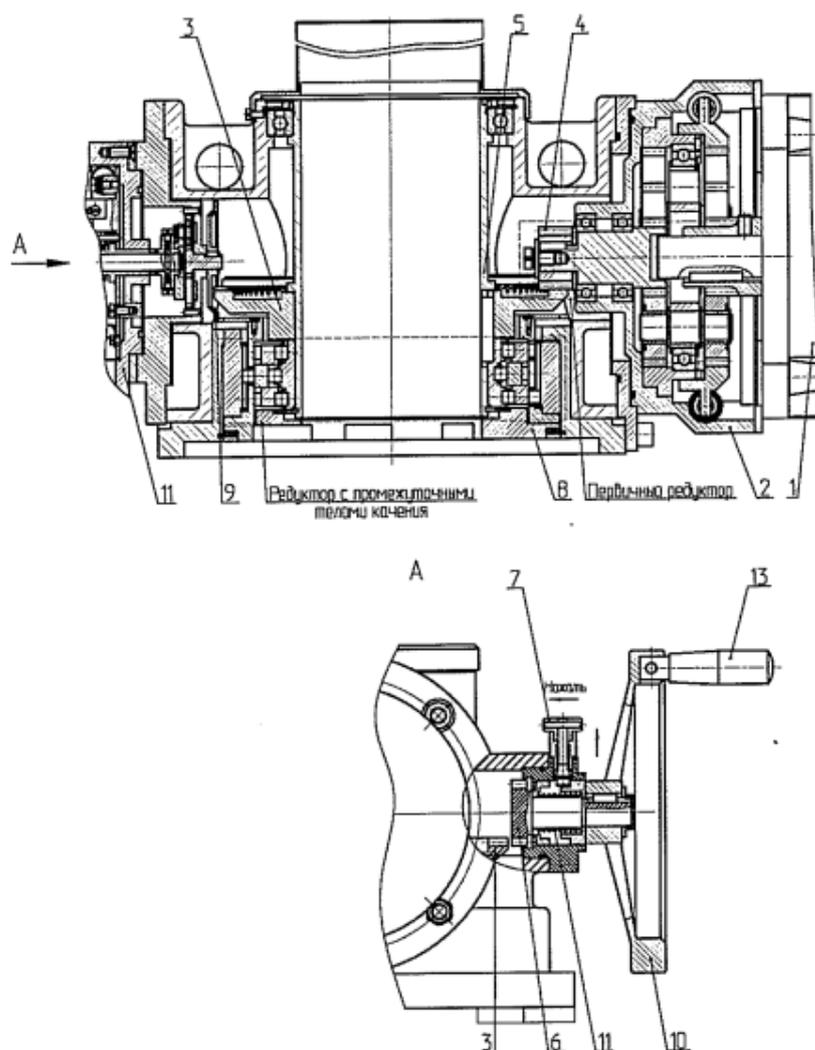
Редуктор электроприводов «ЭПЦМ-10000»с приводом ручного дублера
